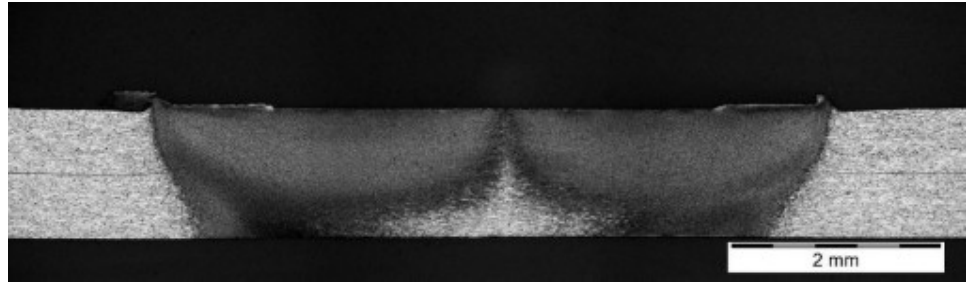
Exemple d'une soudure d'AA7075-T6, sans joint adhésif (décapée)
